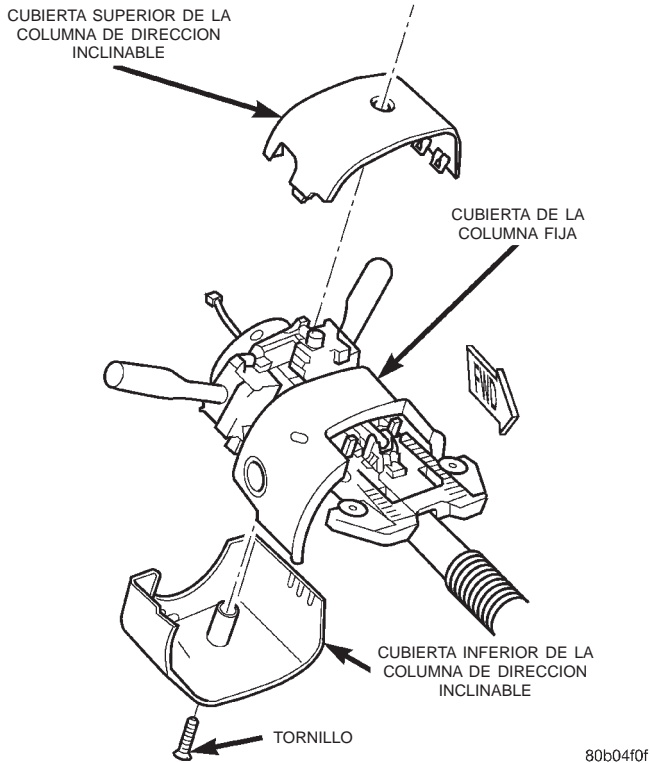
Desmontaje e instalación de la cubierta de la columna de dirección
